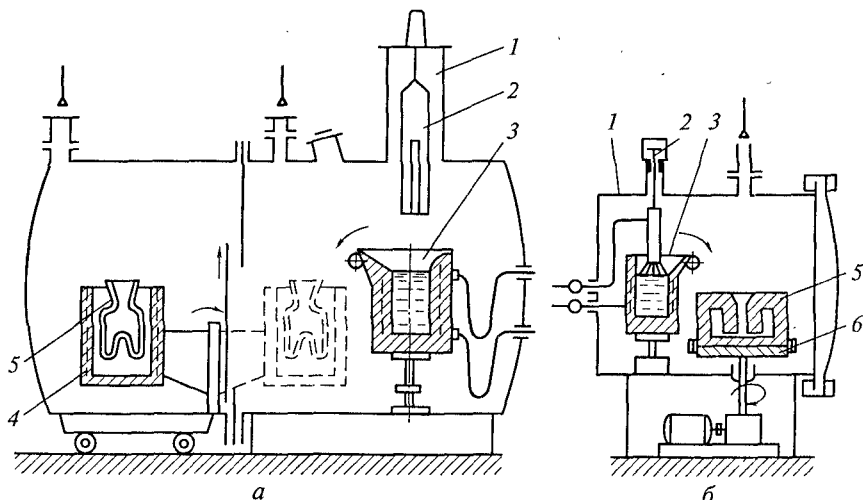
Схемы устройства вакуумных плавильно-заливочных установок: а — с печью подогрева форм; б — с центробежной машиной; 1 — вакуумная камера; 2 — устройство для загрузки шихты; 3 — плавильная печь; 4 — печь подогрева; 5 — форма; 6 — центробежная машина
